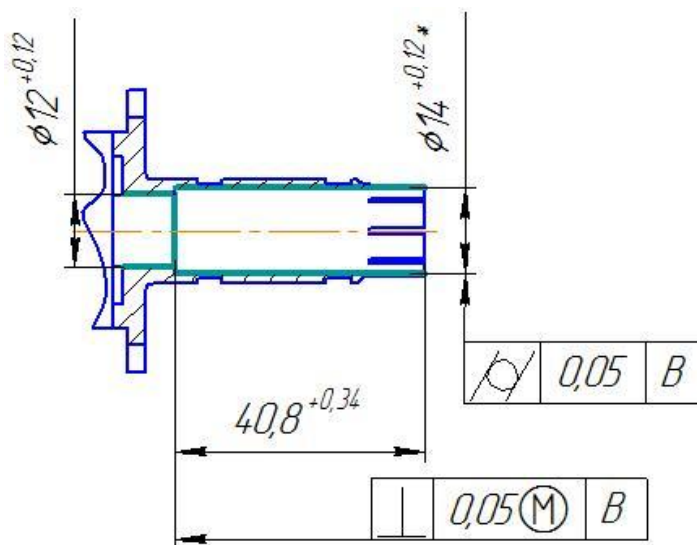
Эскиз обрабатываемого отверстия
